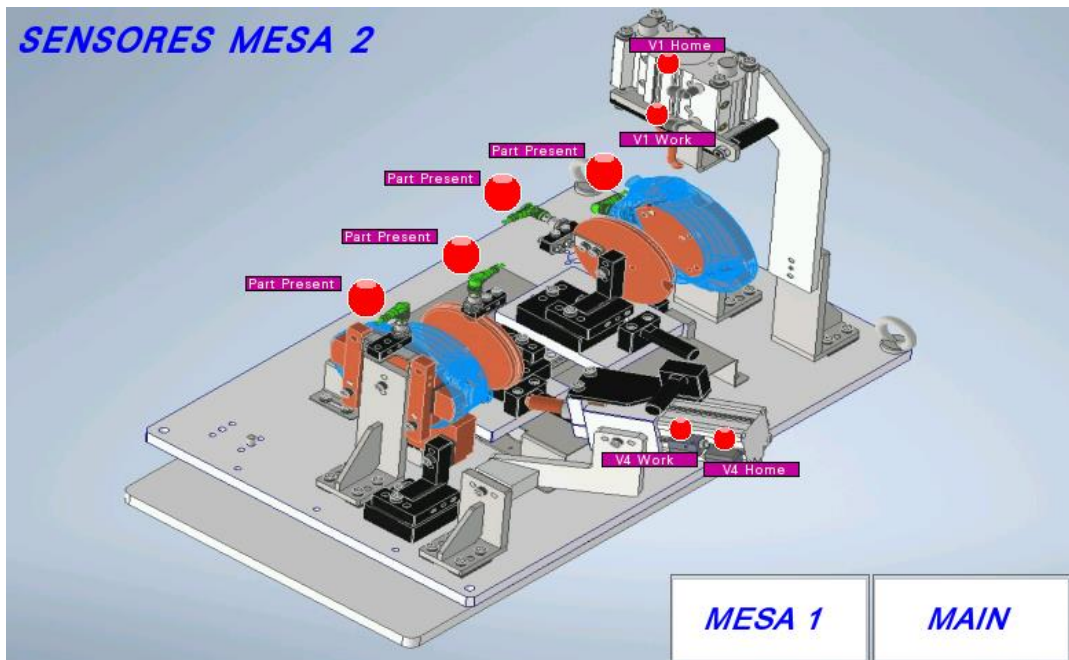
Layout completo mesa 2. Fuente. elaboración propia
